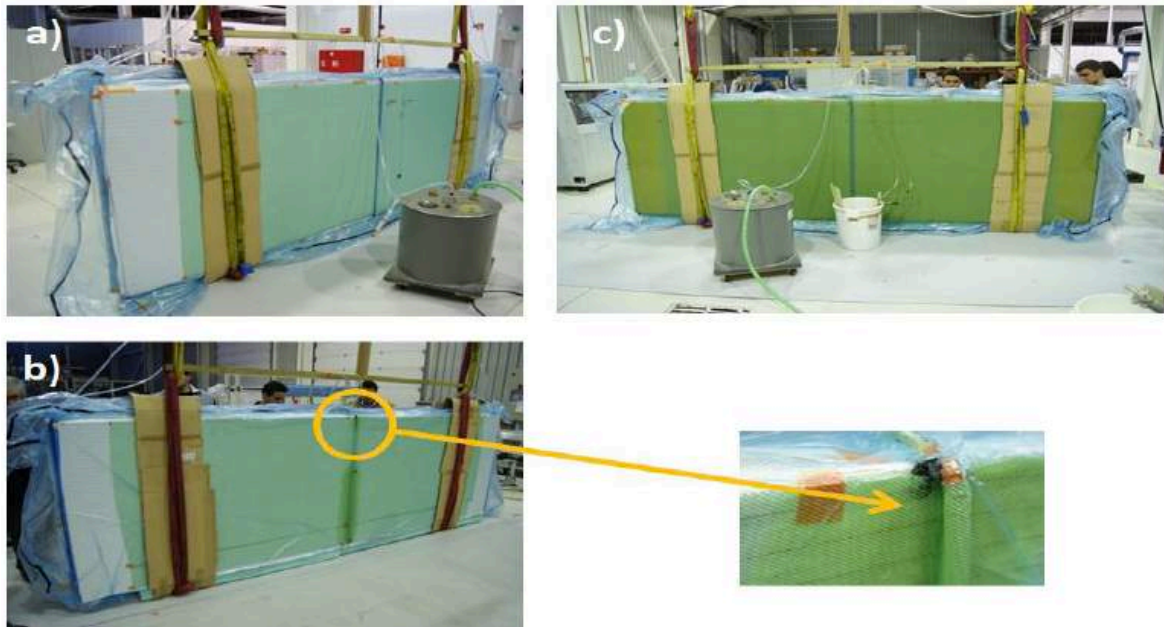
Fabrico dos painéis sanduíche: a) montagem; b) injeção de resina e pormenor do tubo de injeção; c) painel produzido [24].
